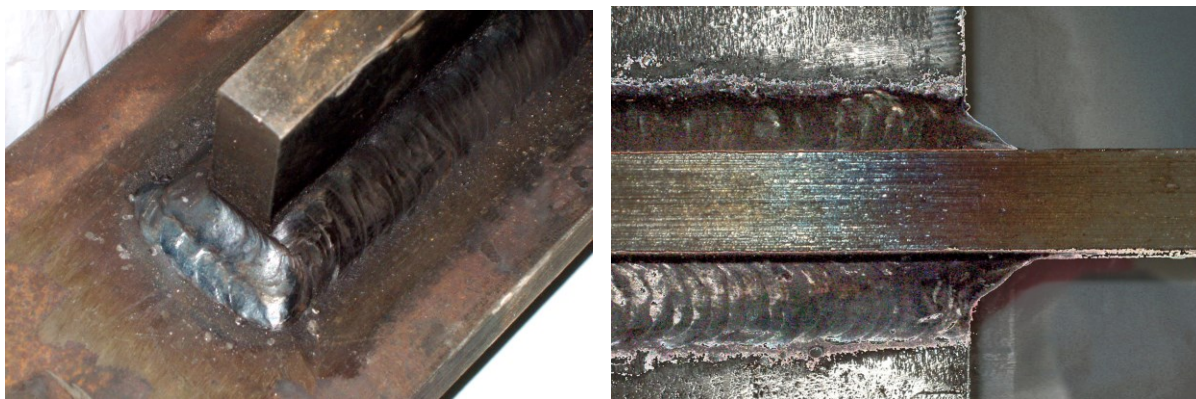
Сварные швы образцов с приваренными планками (рисунок 4.1б) перед испытаниями
